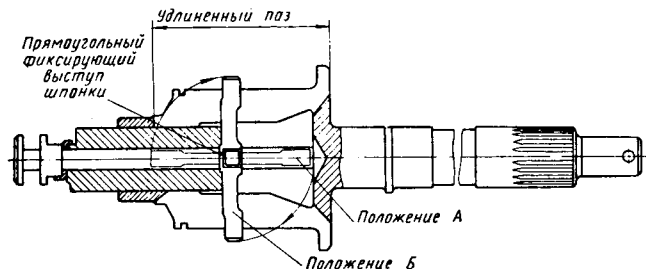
Схема извлечения крестообразной шпонки из пазов вторичного вала коробки передач
